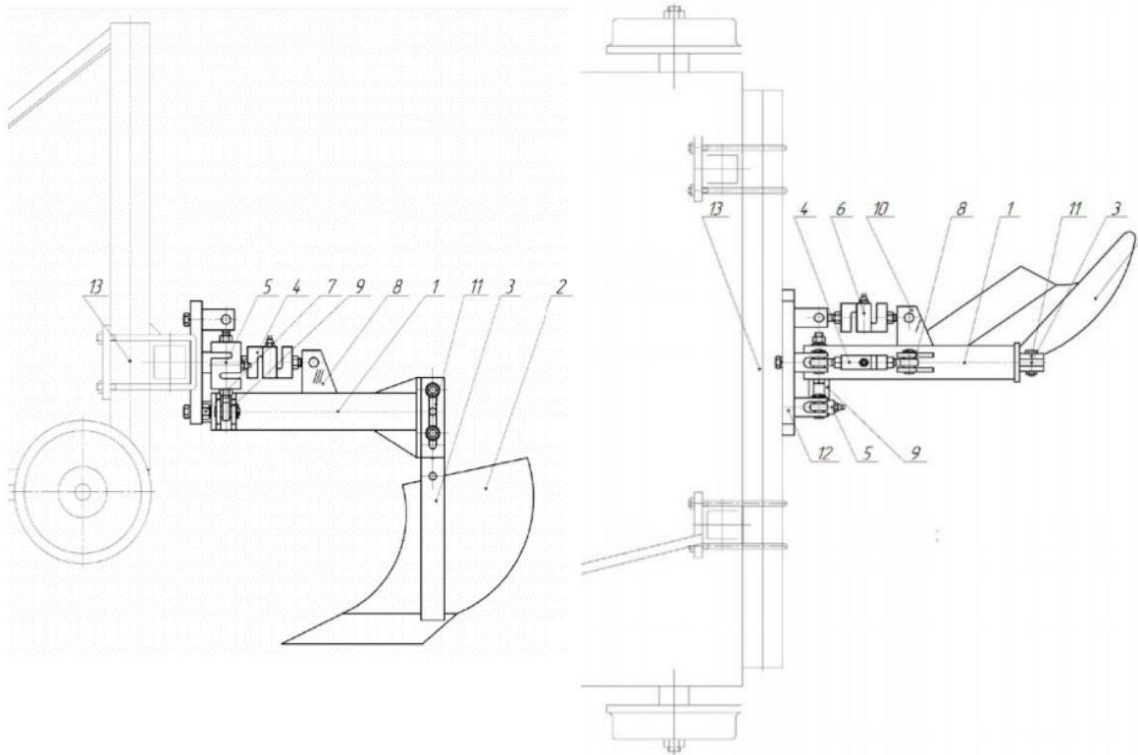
Дослідний візок зі встановленим модулем просторового динамометрування корпусу плуга, що розглядається: а) вид збоку; б) вид зверху
